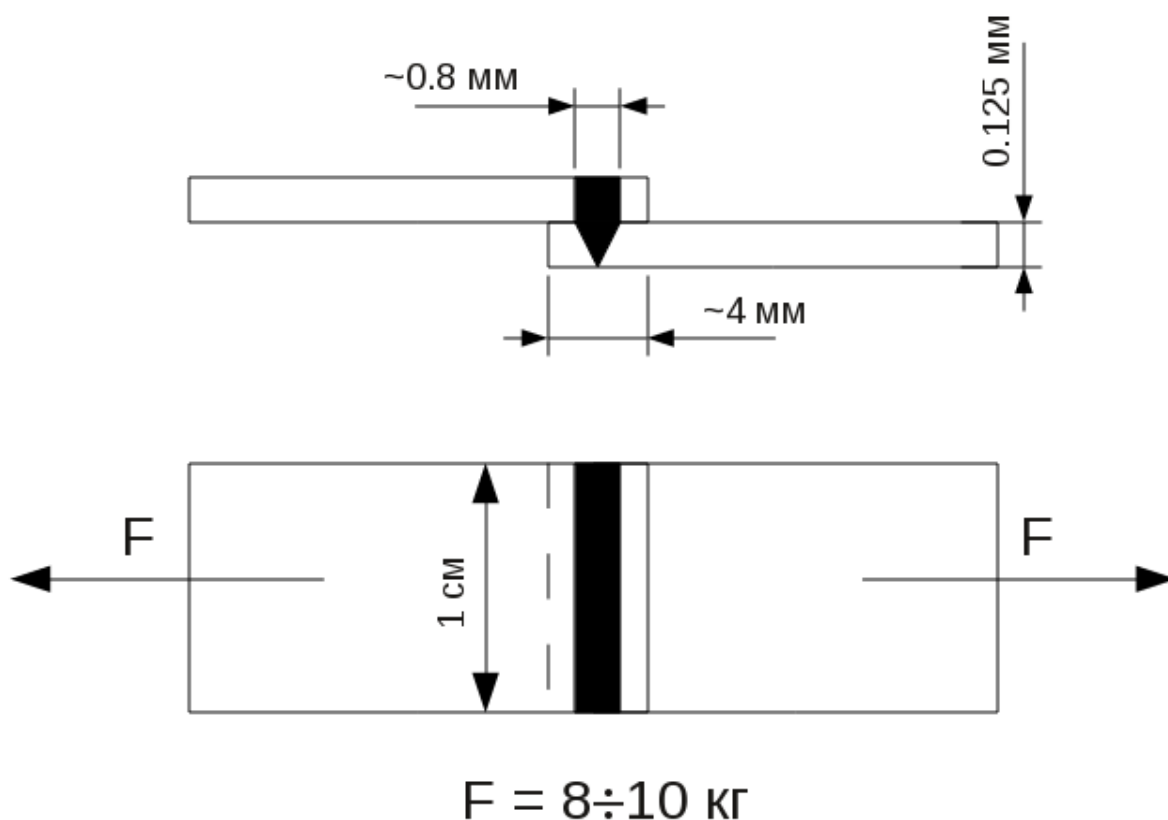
Схематическое изображение сварного шва и испытание его на прочность
